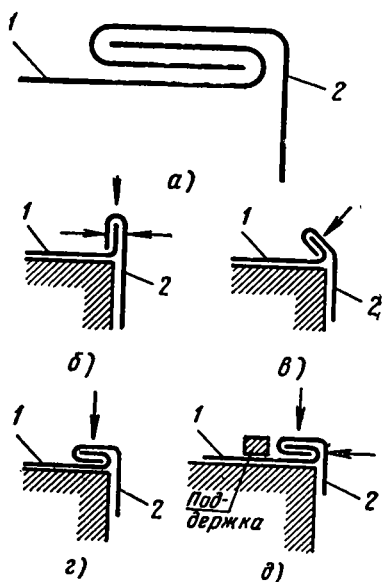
Изготовление углового одинарного фальца ручным способом:
